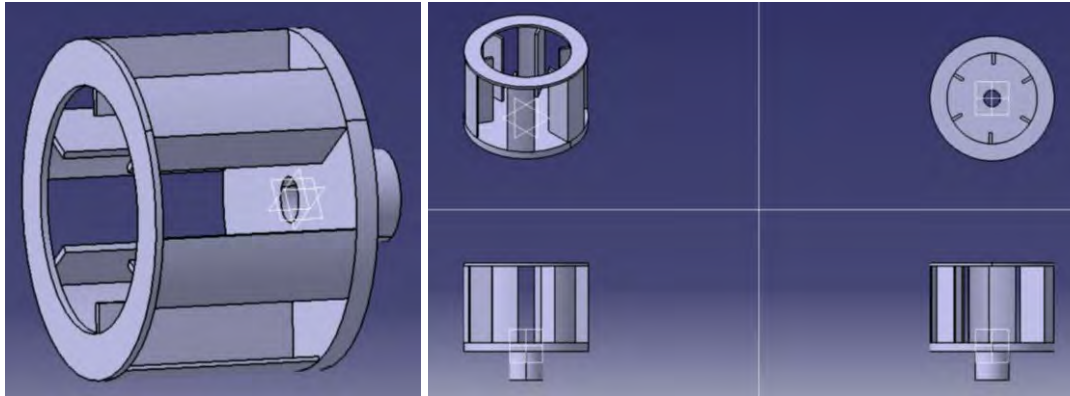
Vistas del dibujo mecánico del soplador (realizado en Catia V5)
